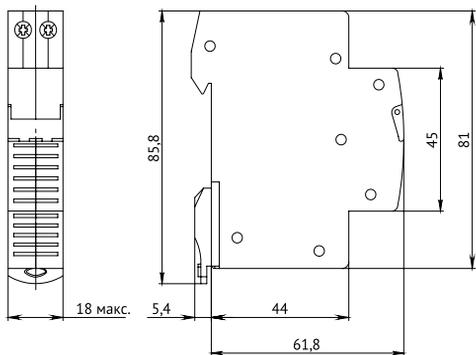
Габаритные, установочные и присоединительные размеры звонков.
